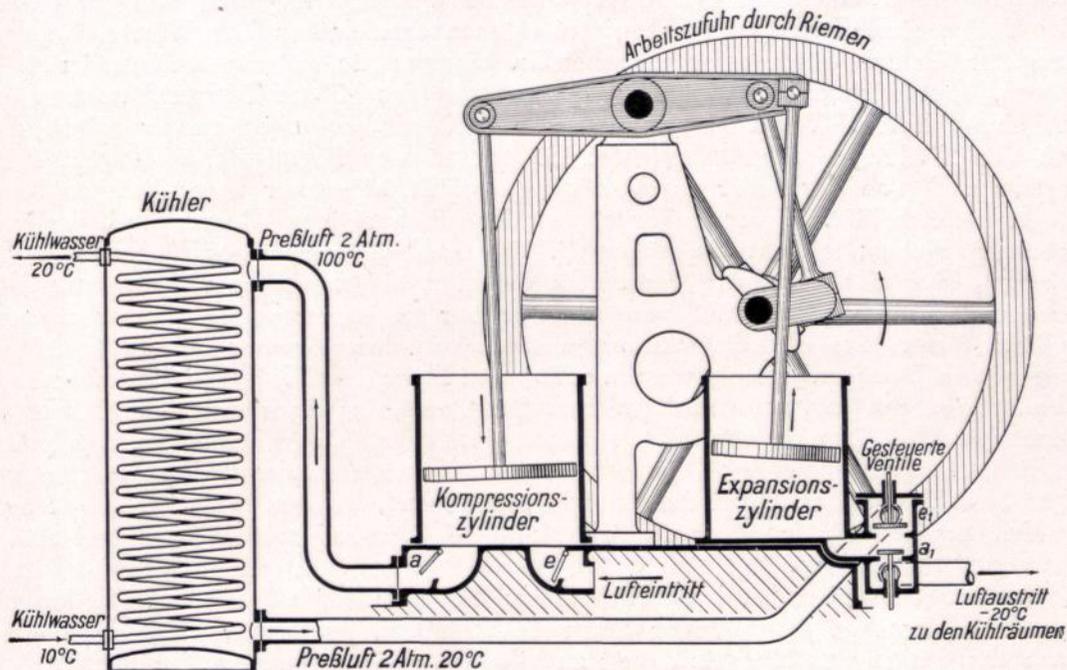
Kaltluftmaschine. Der äußere Aufbau läßt die Maschine als Umkehrung der in Abbildung 41 dargestellten Heißluftmaschine erkennen.
